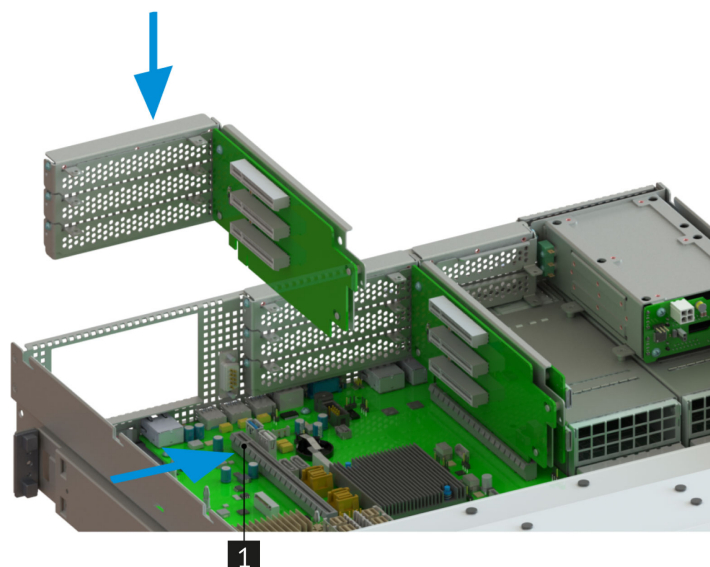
Установка PCIe-райзера с основанием в корпус сервера
